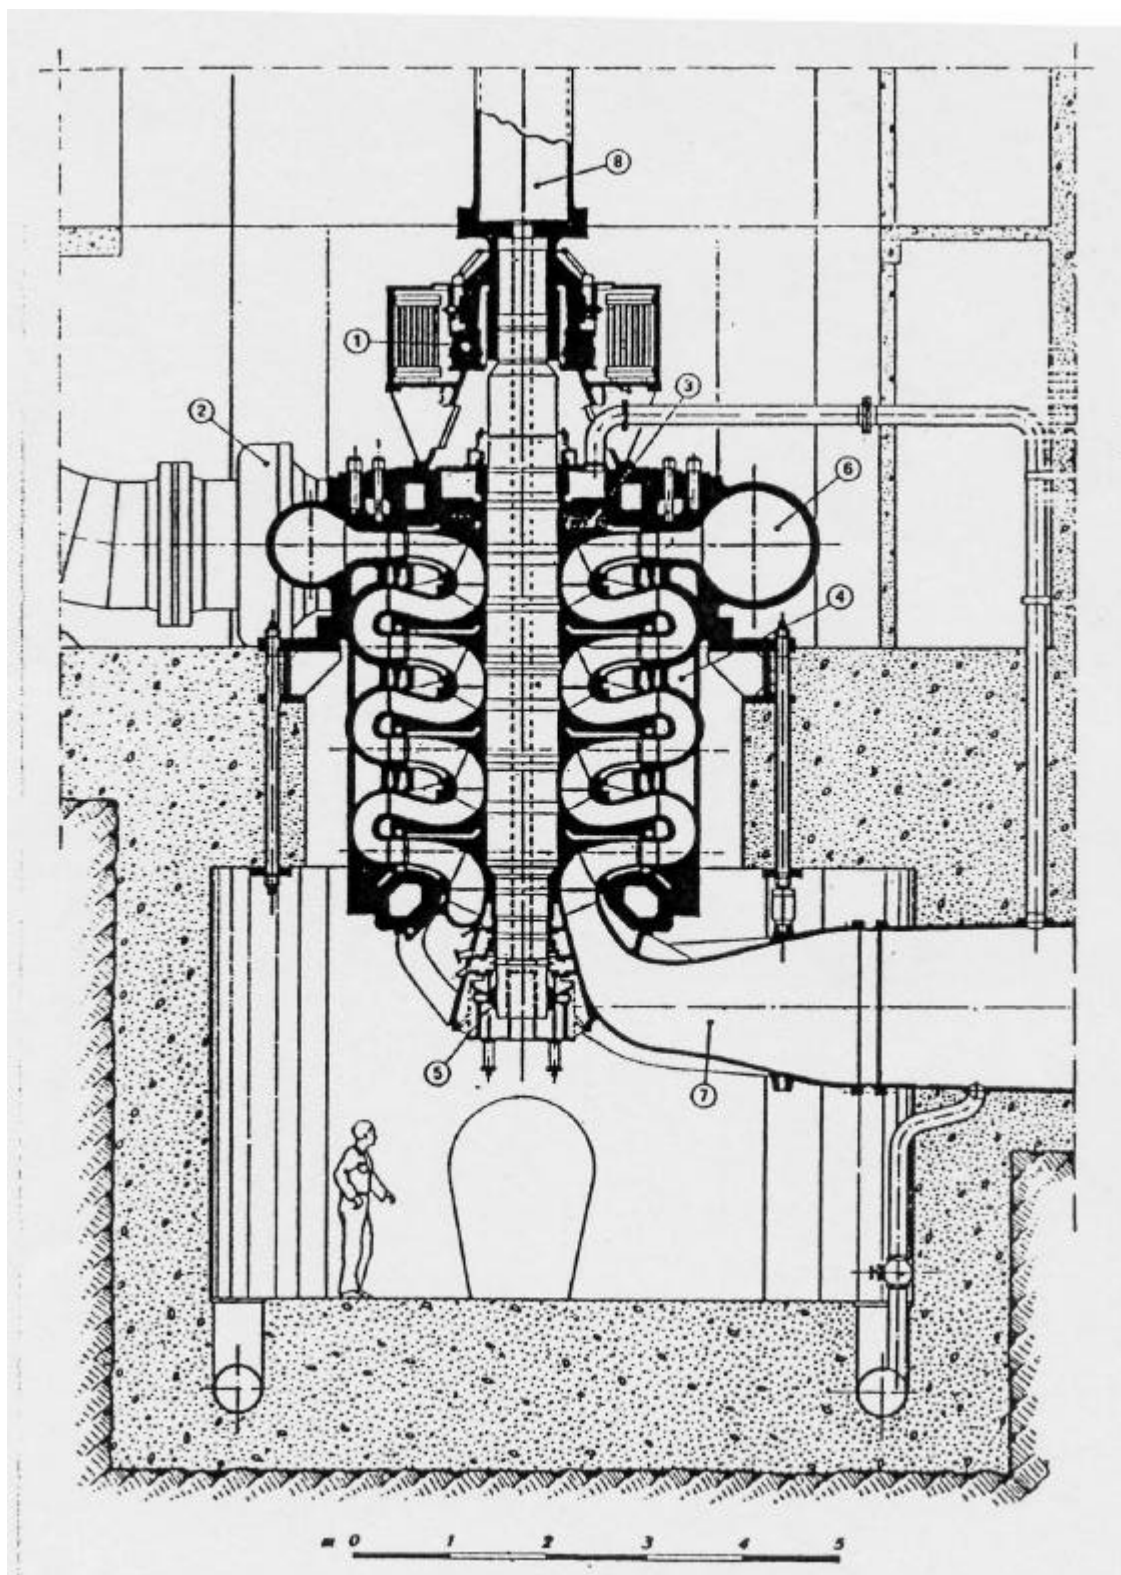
Sezione longitudinale di una pompa di accumulazione dell’impianto del Lago Delio (Asgen-Franco Tosi).
